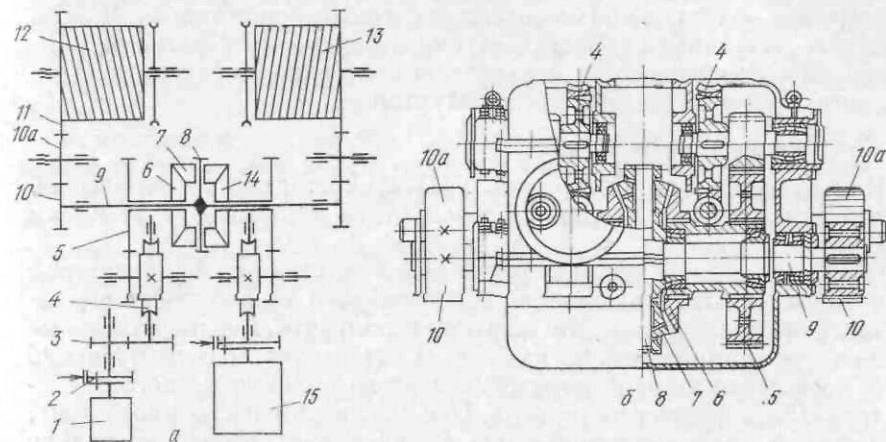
Кинематическая схема (а) и дифференциальный редуктор (б) механизма кантования
